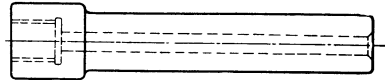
Halter mit Gewinde für Tieflochbohrer.
